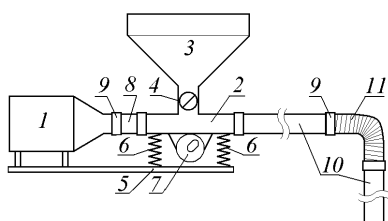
Пневмотранспортная установка для уборки снега с крыши [11]
